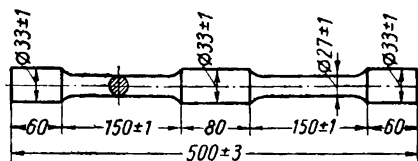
Чертеж поковки к примеру расчета ручьев для вальцовки заготовки
